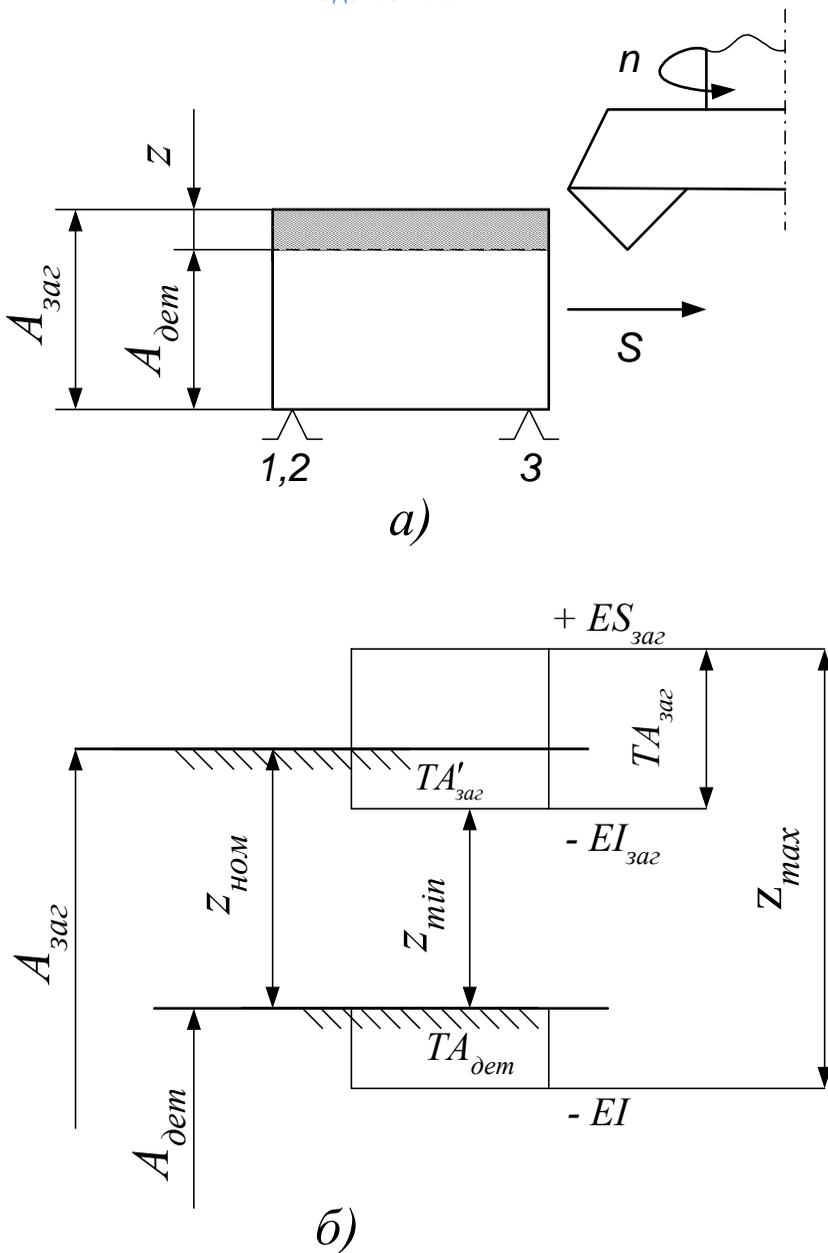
Схема торцевого фрезерования плоскости и расчетная схема для определения охватываемого размера заготовки
